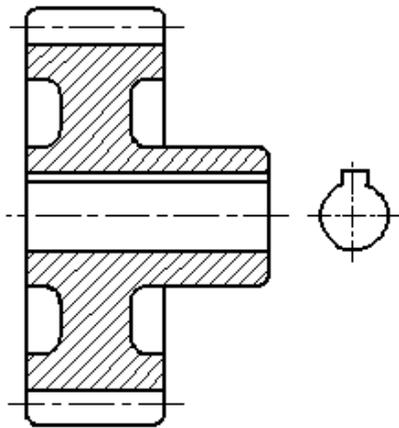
Образец изображения отверстия в ступице зубчатого колеса
